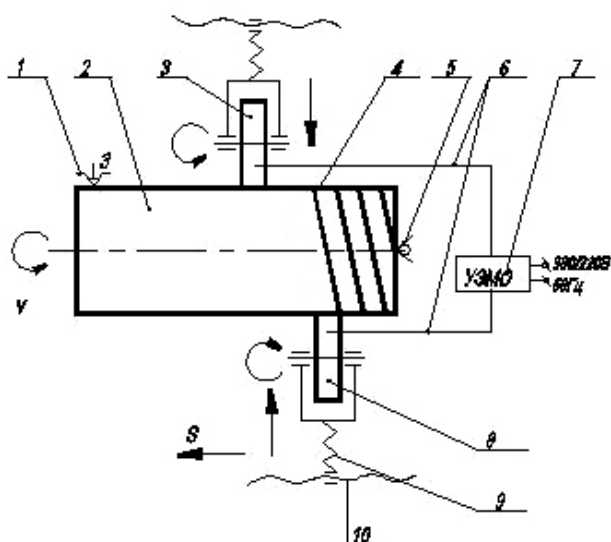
Принципиальная схема электро-механической поверхностной заправки гладких цилиндрических поверхностей: 1 – трехкулачковый самоцентрирующий патрон; 2 – заготовка; 3 – ролик токоподводящий; 4 – обработанная поверхность; 5 – центр вращающийся; 6 – кабели (шины) токоподводящие; 7 – установка ЭМО; 8 – инструментальный ролик; 9 – державка телескопическая; 10 – ходовой винт станка.
